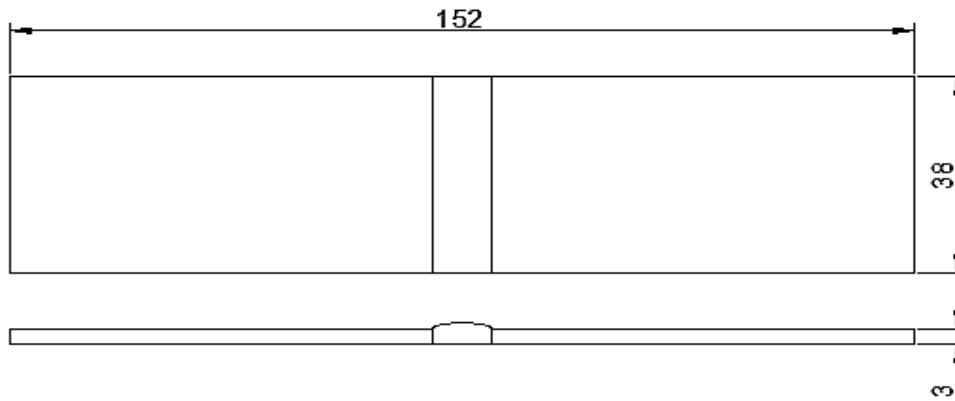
Probeta para ensayo de doblado (Medido en mm)
